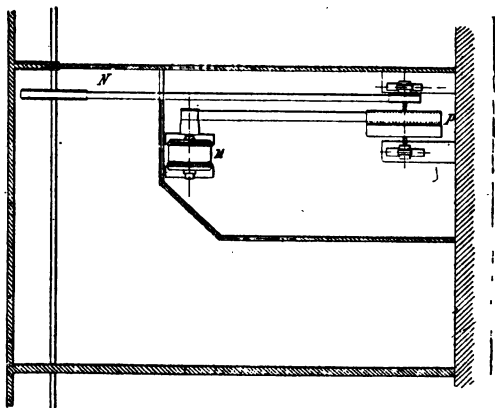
bis. — Plan de l'installation du moteur dans les ateliers Mildé.
